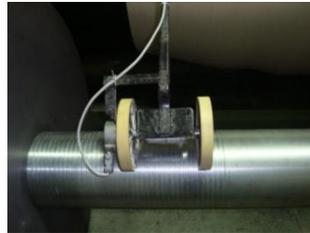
Dispositivo utilizado para contar el metraje en el plegado.
